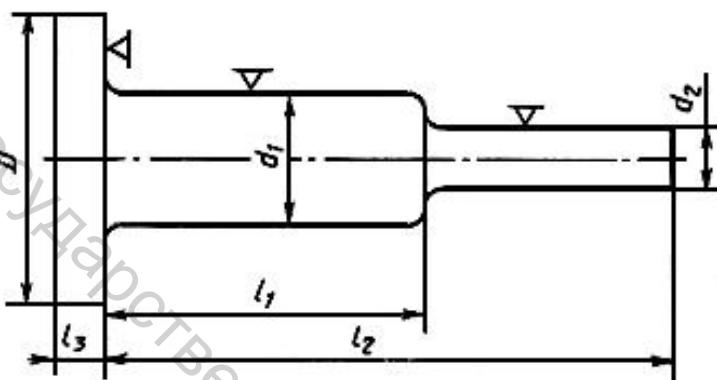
Правила простановки размеров на чертеже штампованной заготовки
